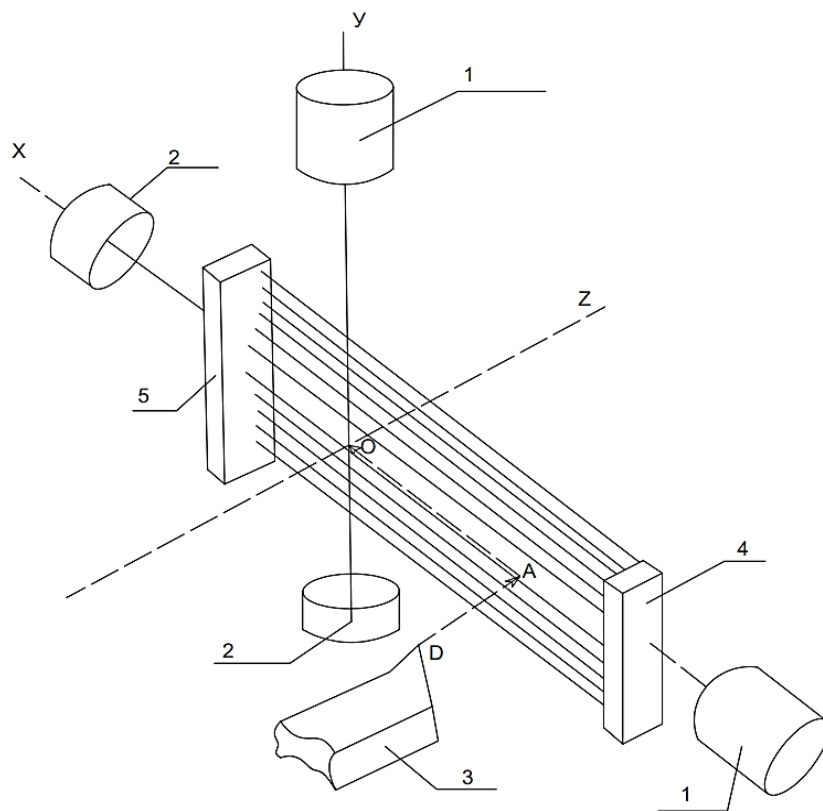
Схема автоматической настройки токарного станка с ЧПУ предлагаемым способом
